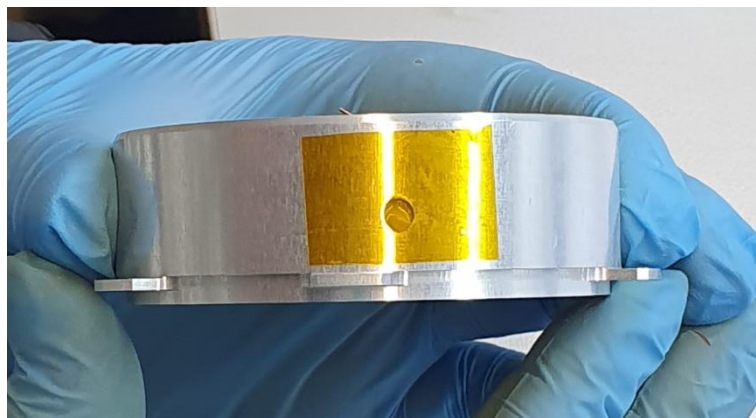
Корпус статора с закрытым отверстием для введения клея.
